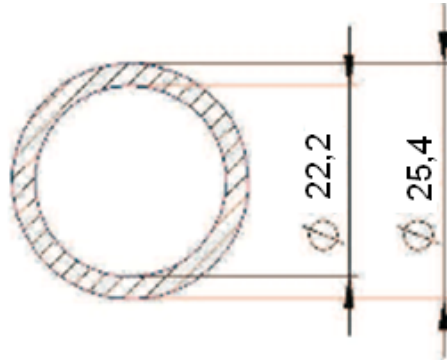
Dimensiones geométricas del tubo de acero estándar
